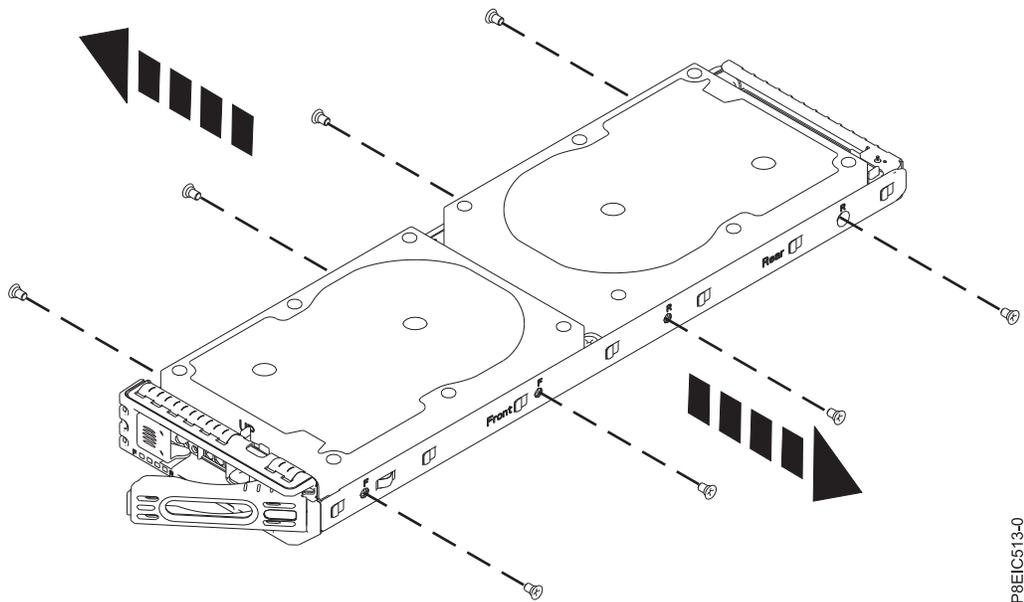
Schrauben vom 3,5-Zoll-Laufwerk entfernen
